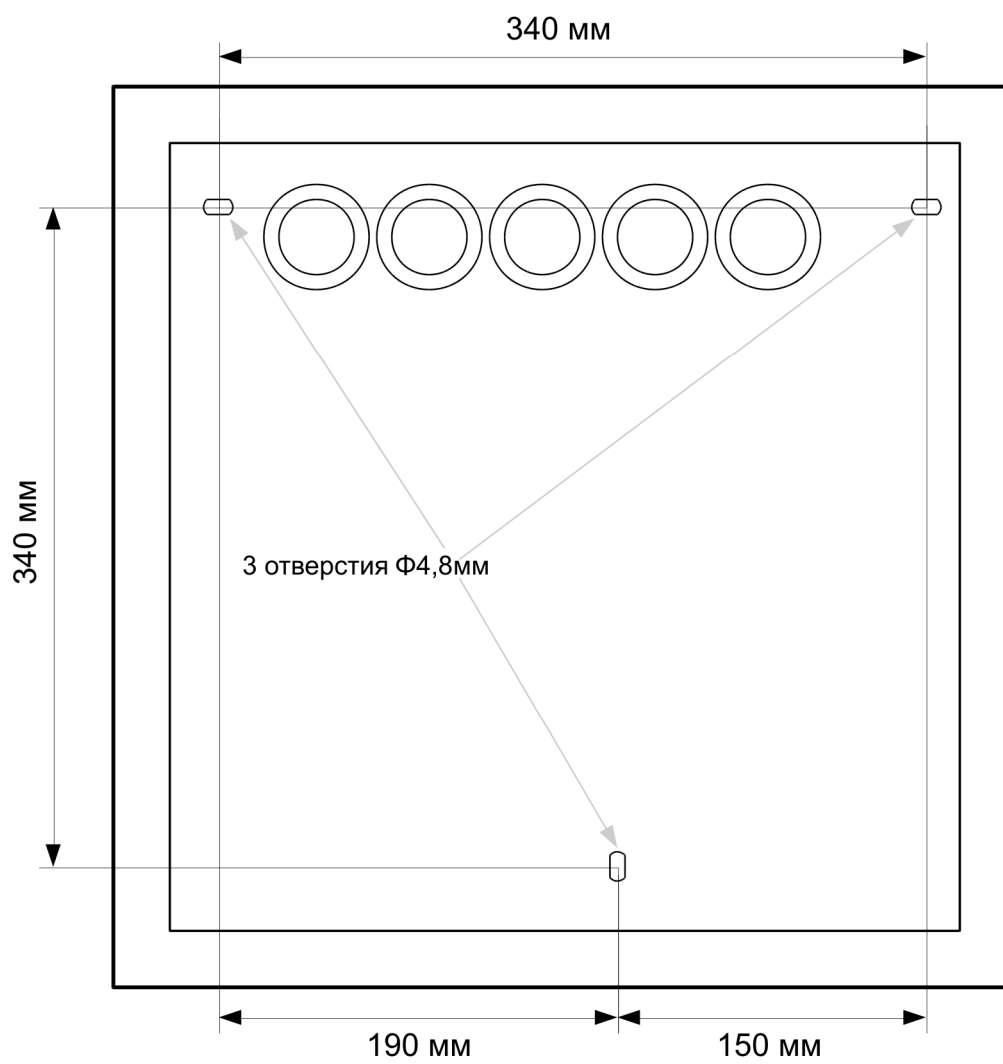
Крепление прибора UCS в корпусе до 16 А.
